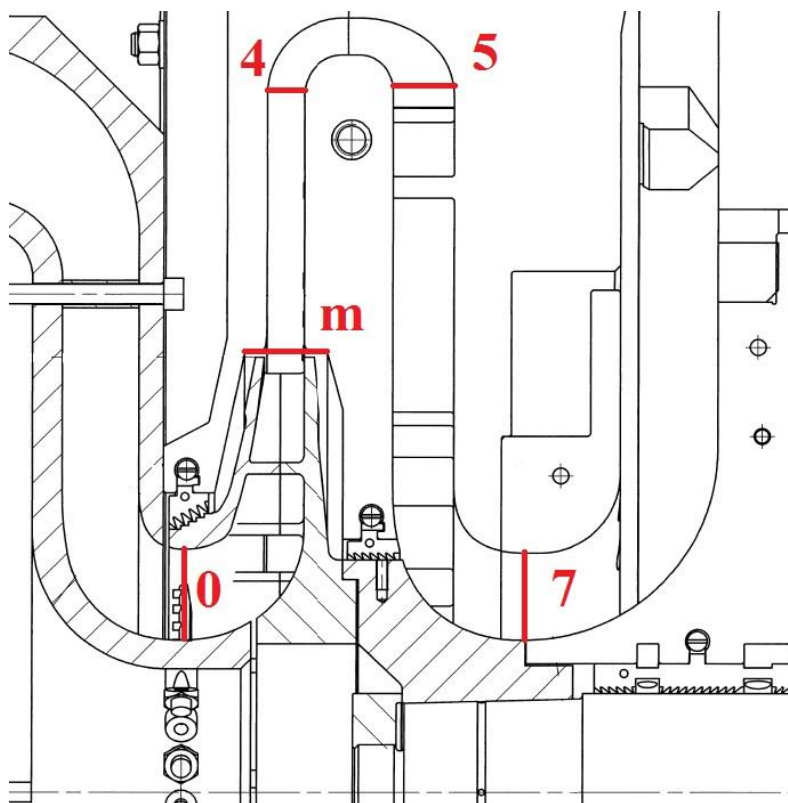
Rotor kompresoru<sup>2</sup>
